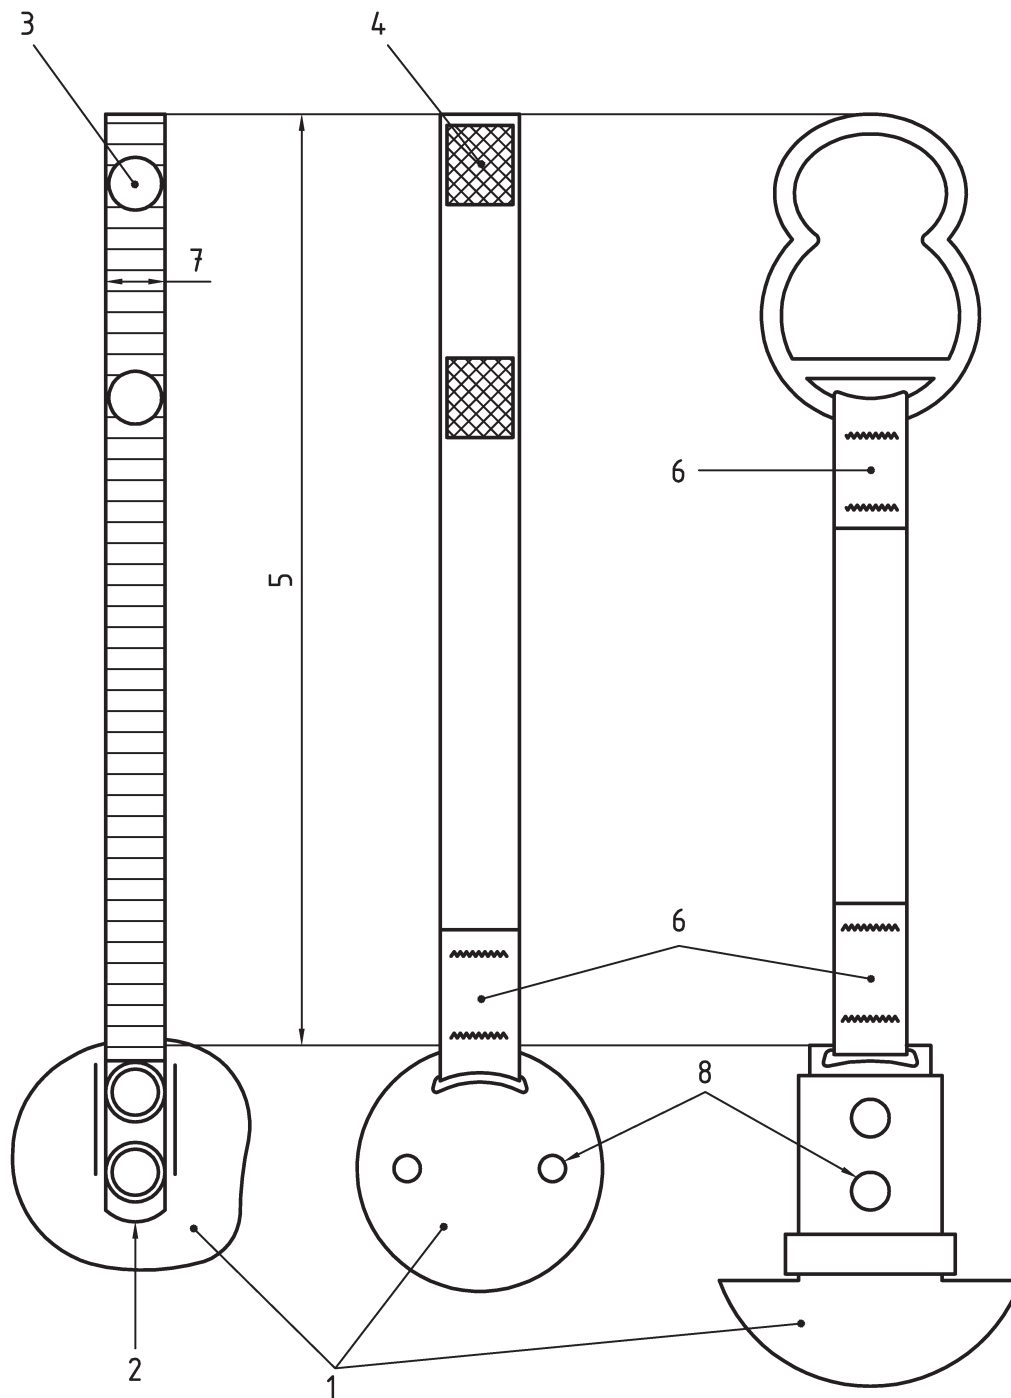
Typische Ausführungen von Schnullerhaltern, die an Schnullern montiert sind
